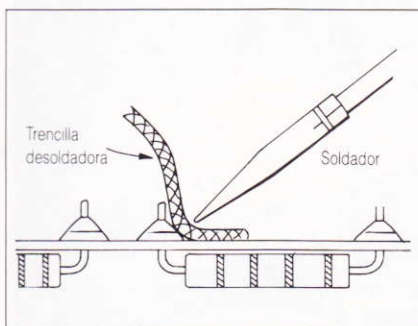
Para desoldar puede emplearse trencilla especial para desoldaduras.
